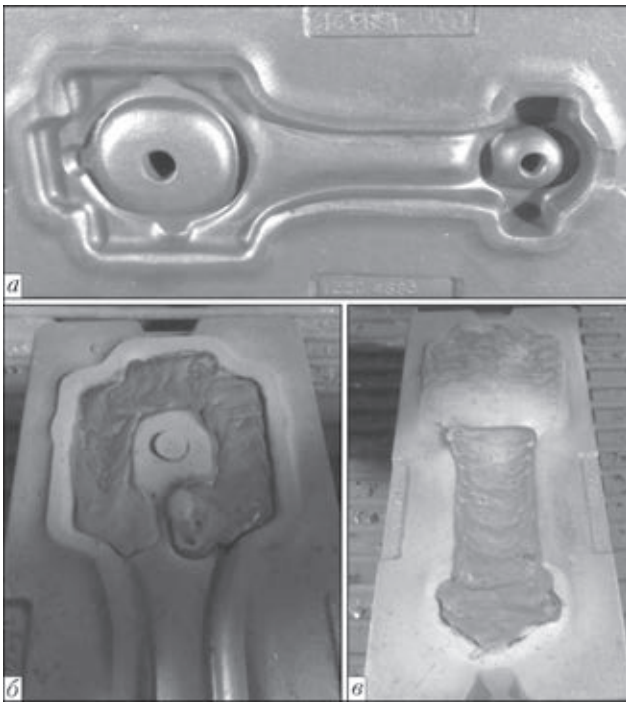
Ремонт штампа детали (шатуна): а — состояние изношенной рабочей поверхности штампа; б — наплавка валика без колебаний; в — наплавка с колебаниями
